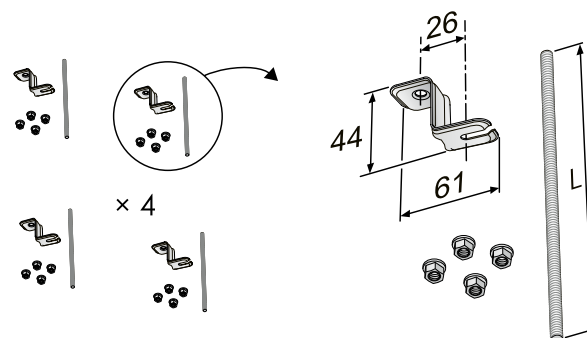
Élément d'assemblage SYST MS M8-1, installation au plafond et sur tige filetée
